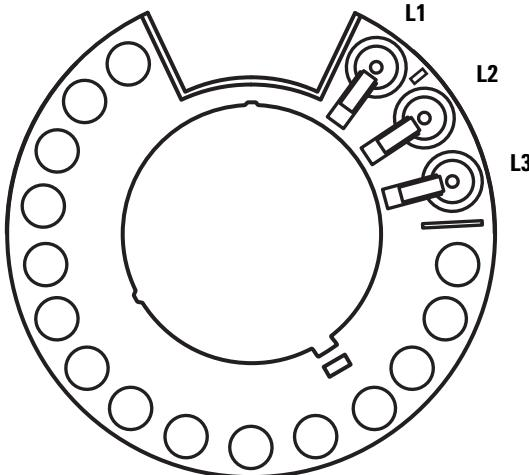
Posizioni L1, L2, L3 della torretta di trasferimento (vista dall'alto)
